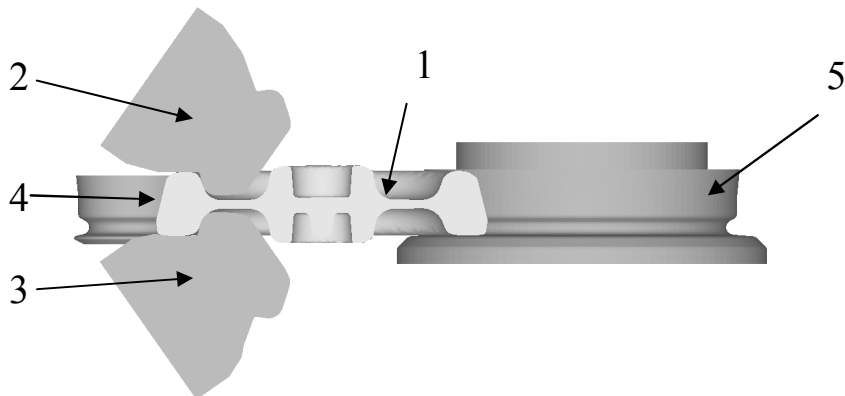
начальный момент осадки обода по ширине наклонными валками: 1 – заготовка колеса перед прокаткой, 2 – верхний наклонный валок, 3 – нижний наклонный валок, 4 – нажимной валок, 5 – коренной валок.
